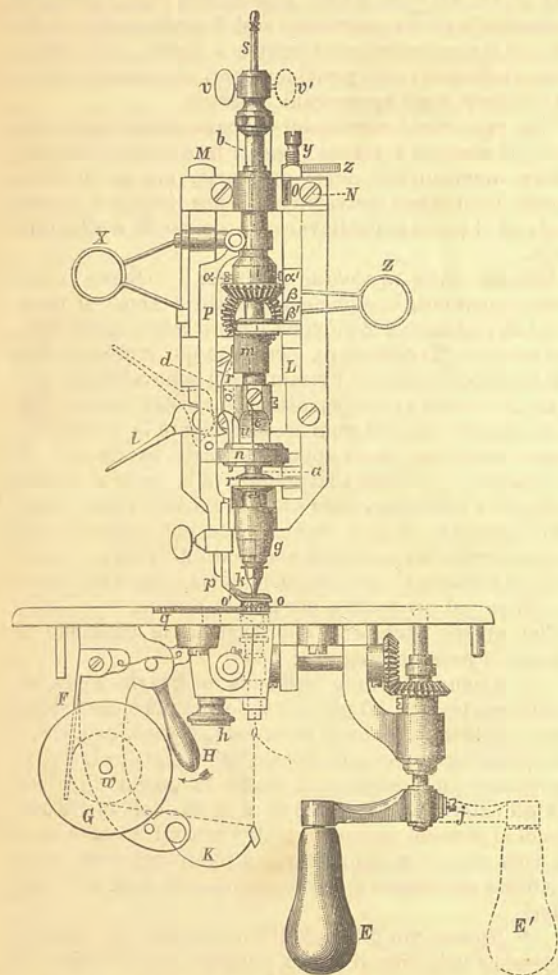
Macchina a ricamare Schürmer, Dlau et O (testata).
